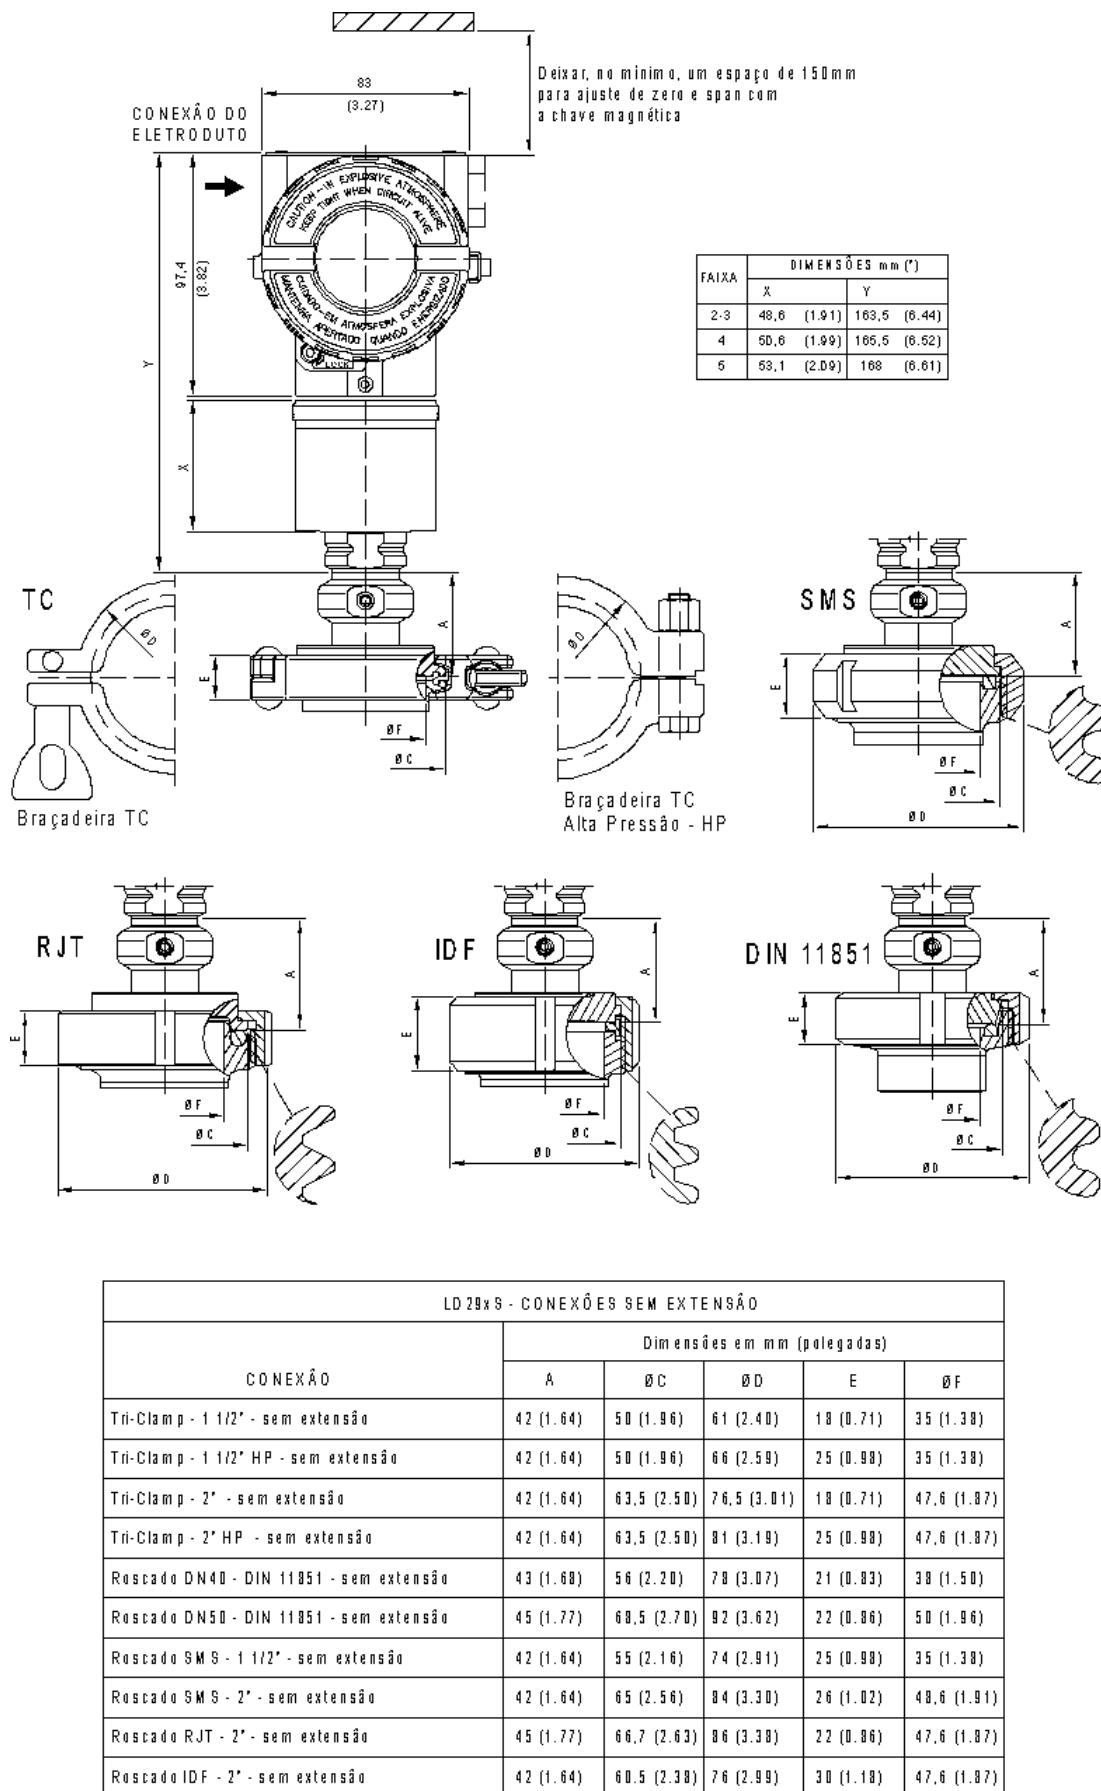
(b)– Desenho Dimensional e Posição de Montagem para o LD293 – Transmissor Sanitário
